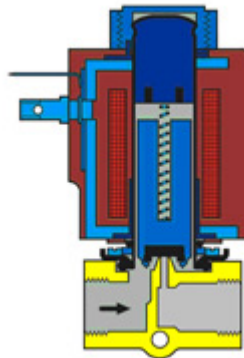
Válvula solenóide composta do corpo e da bobina solenóide
